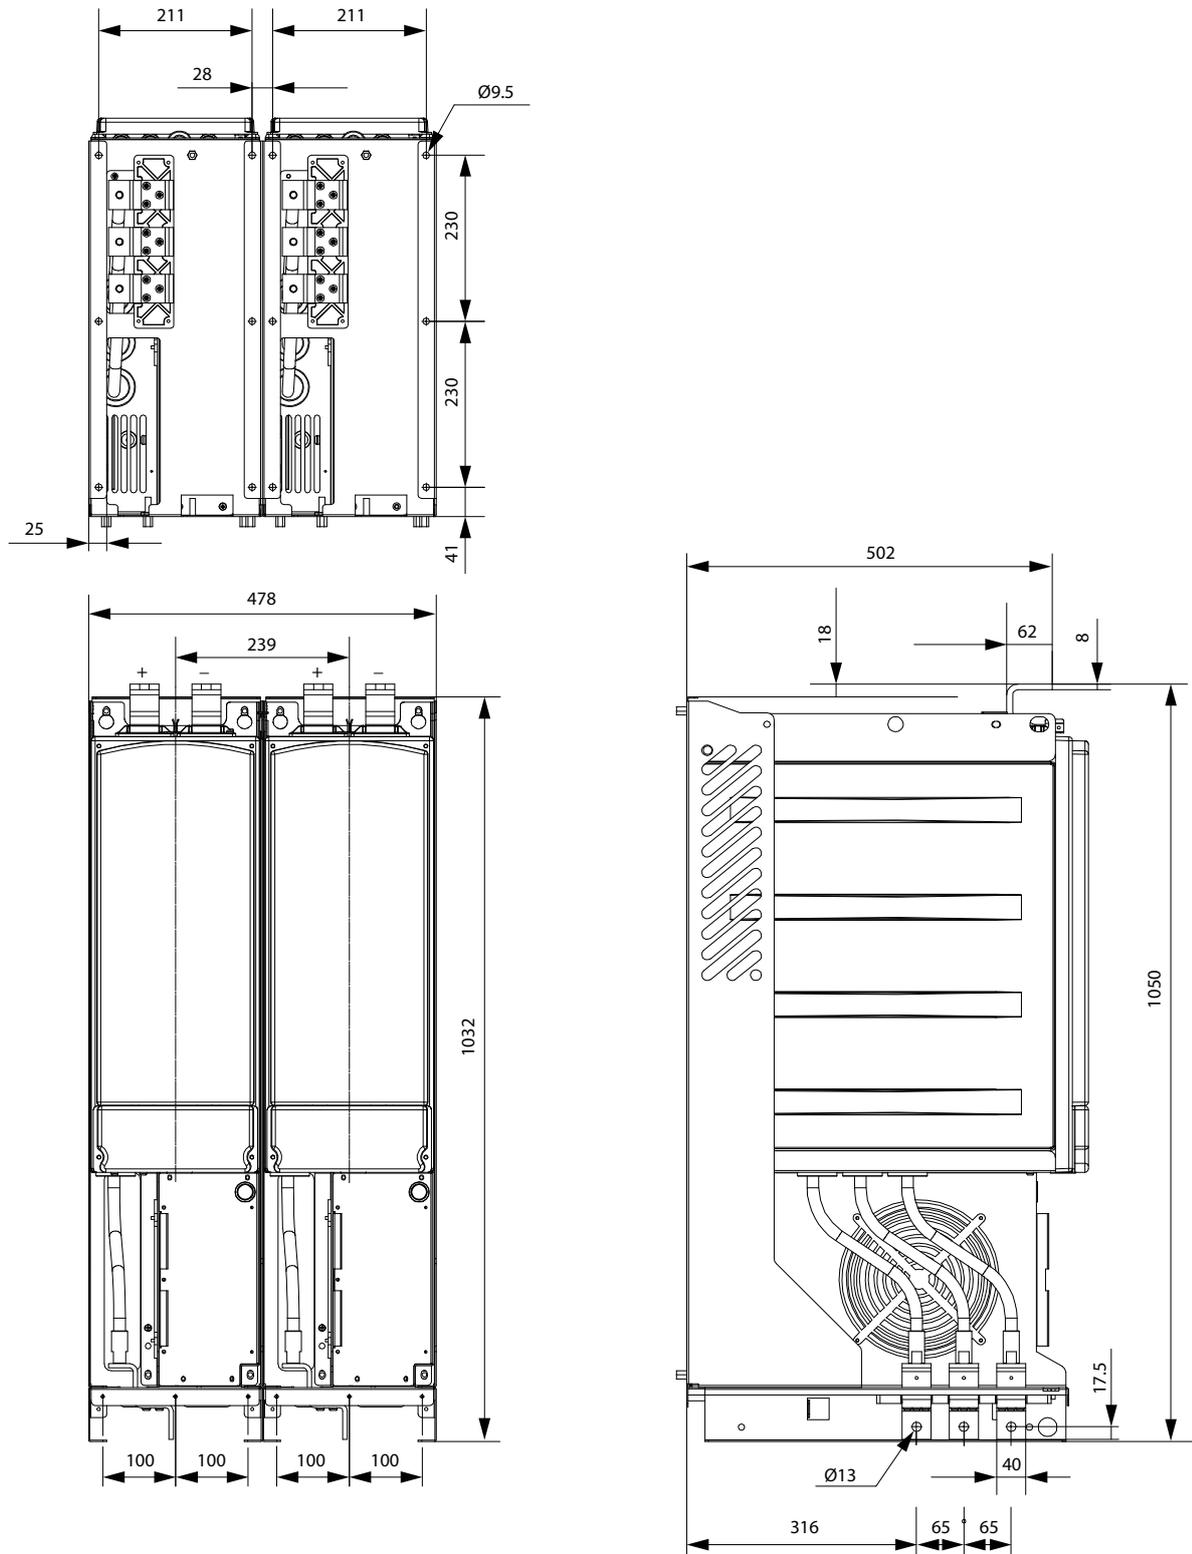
Dimensions du VACON® NX Inverter FI12, vue avant
